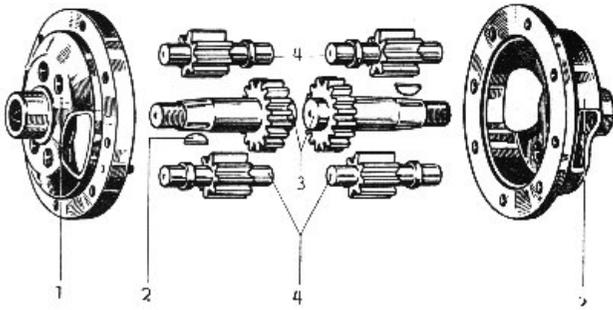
Explosivdarstellung des Ausgleichgetriebes
